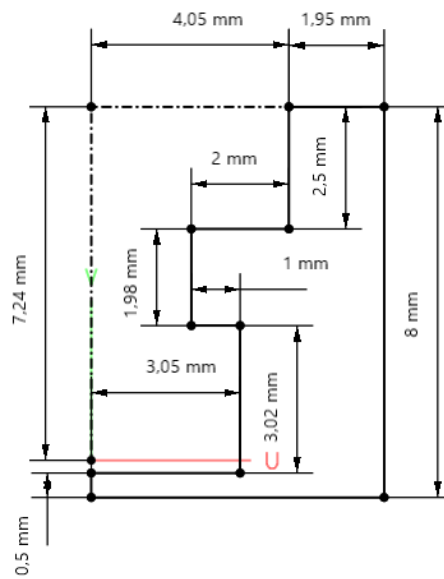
Dimensiones geométricas del soporte de la pieza 7 empleadas para el diseño del boceto usado para la revolución del mismo.
